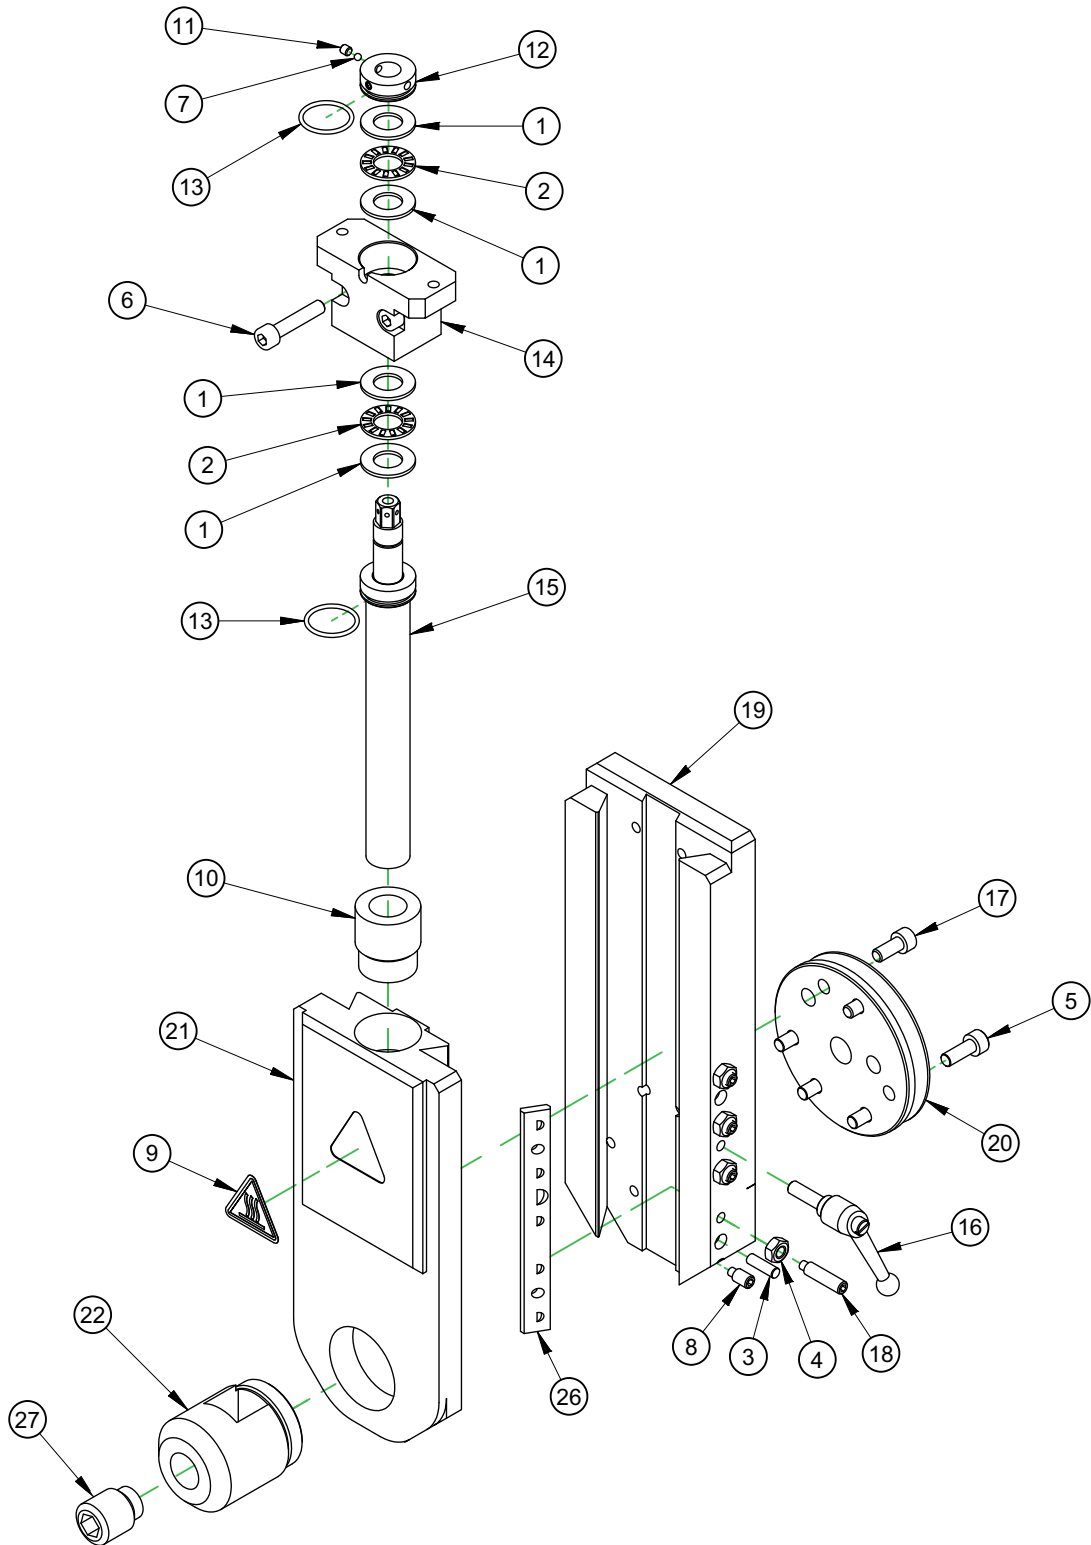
P/N 79790 ENSEMBLE COULISSANT PORTE-OUTIL
